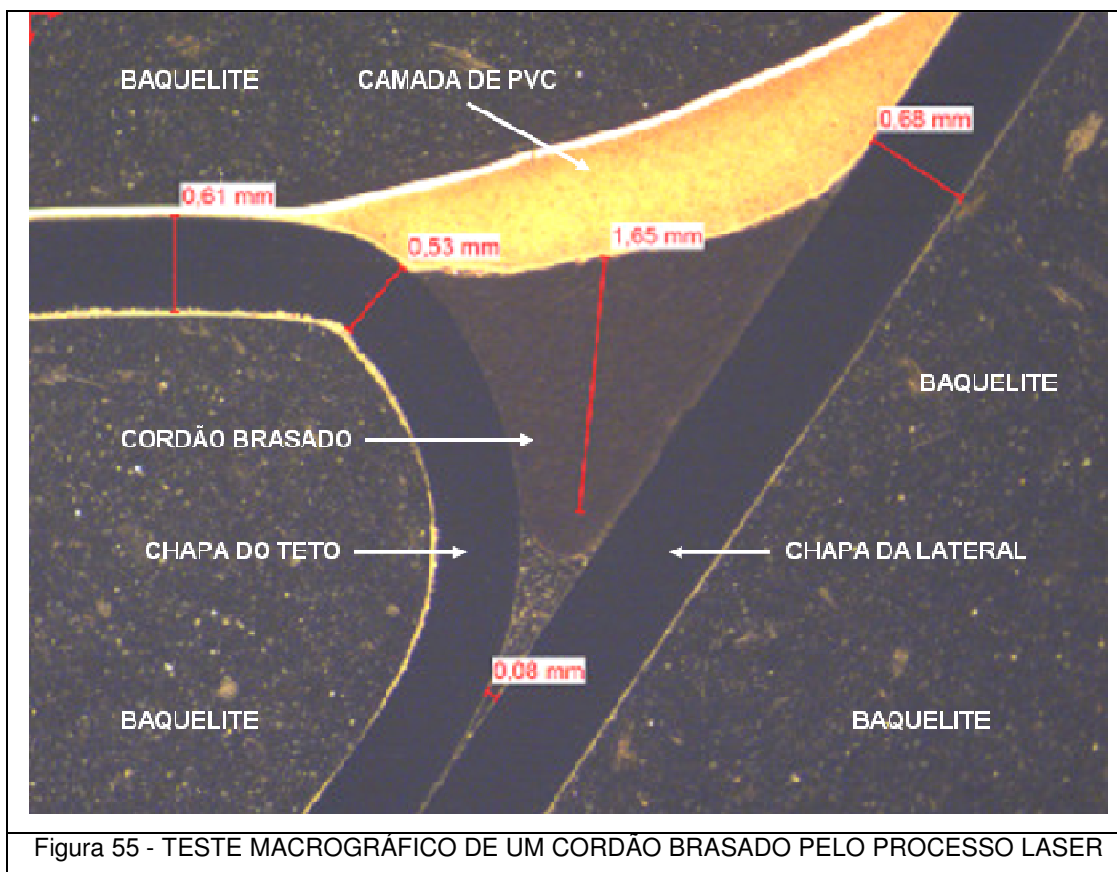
TESTE MACROGRÁFICO DE UM CORDÃO BRASADO PELO PROCESSO LASER
